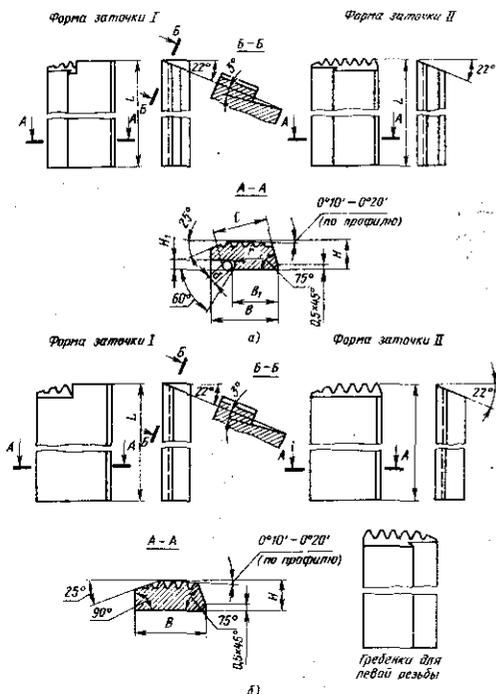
Резьбонарезные плоские гребенки: а – тип А; б – тип В (размеры см. табл. 129).
